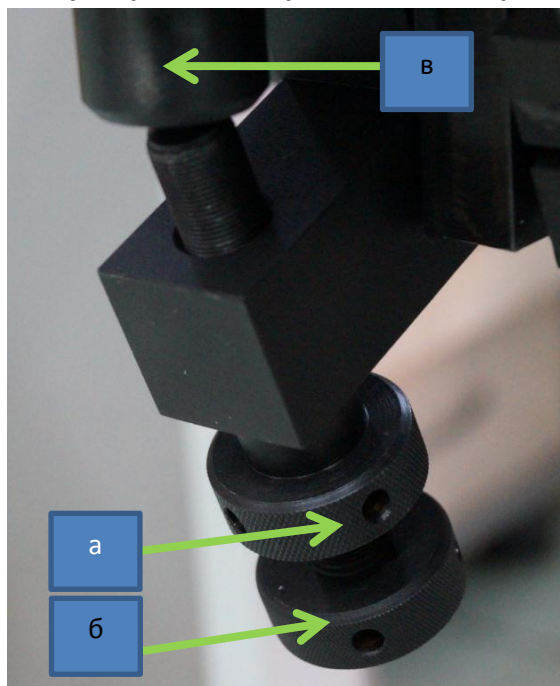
Регулировочный винт обжима. А- контргайка, б- регулировочный винт обжима, в- толкатель
